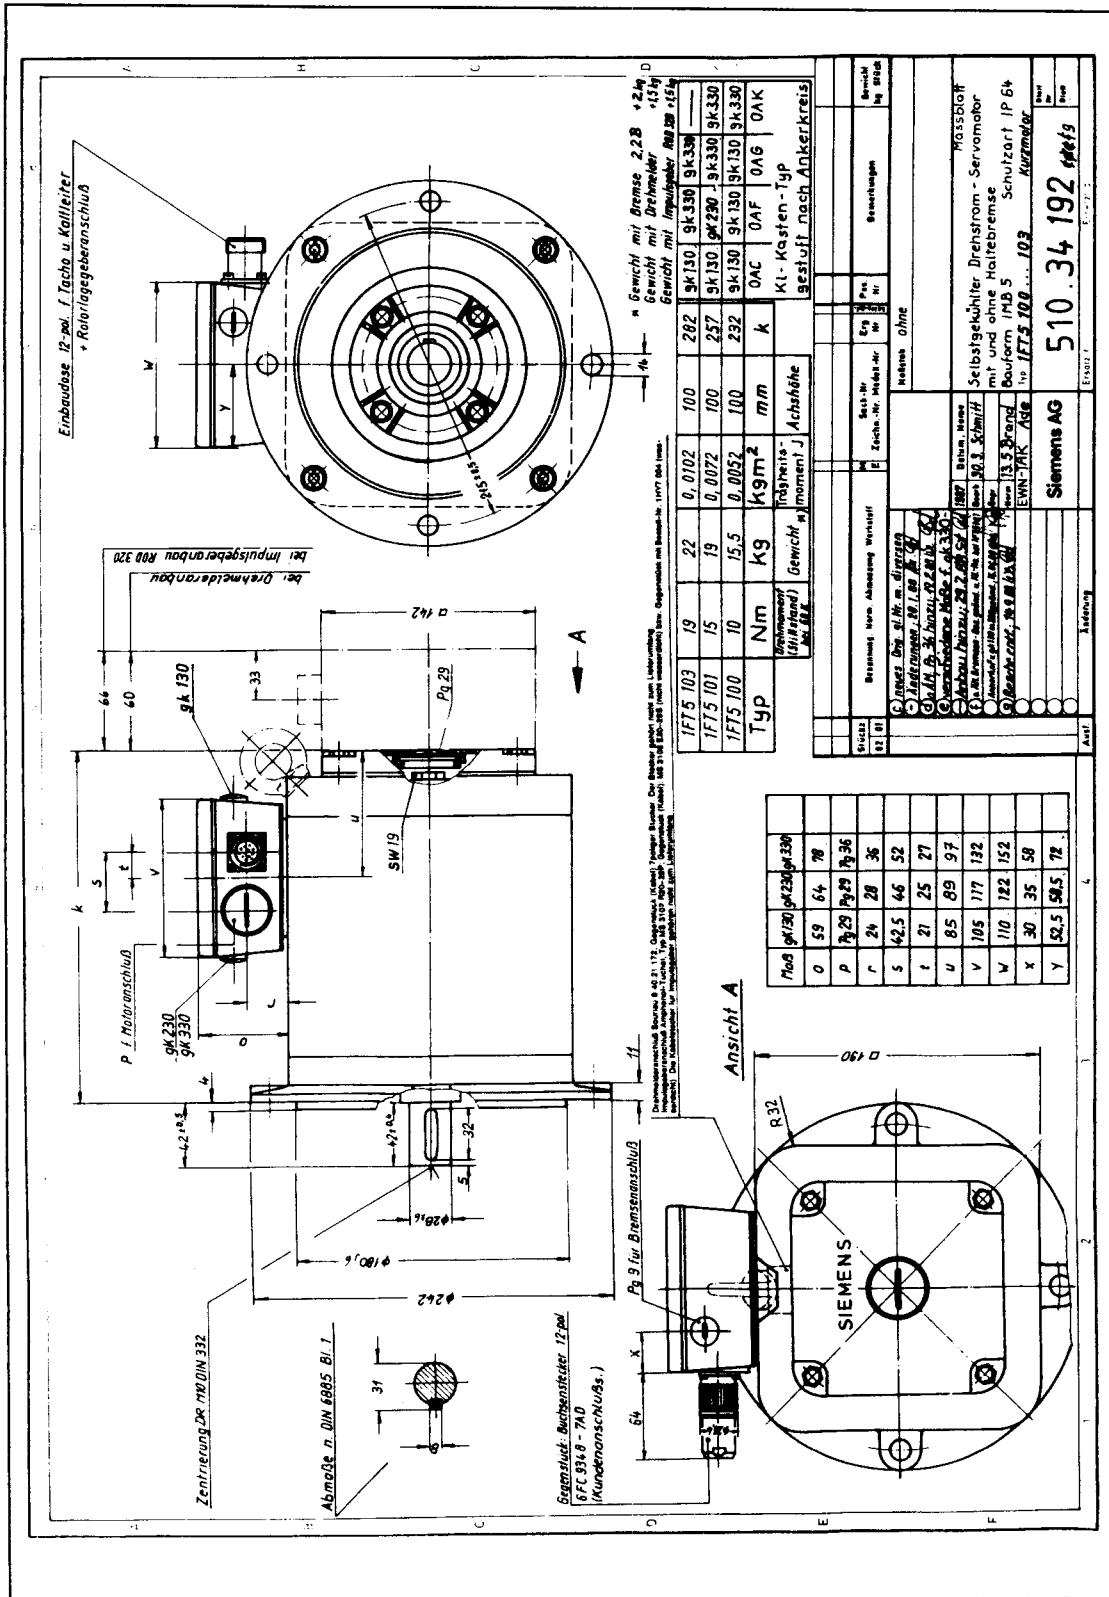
Чертеж серводвигателей переменного тока 1FT5100, 1FT5101 и 1FT5103, конструкционная форма IM B5
